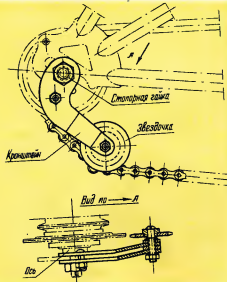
Устройство для регулировки натяжной цепи ногового привода.
